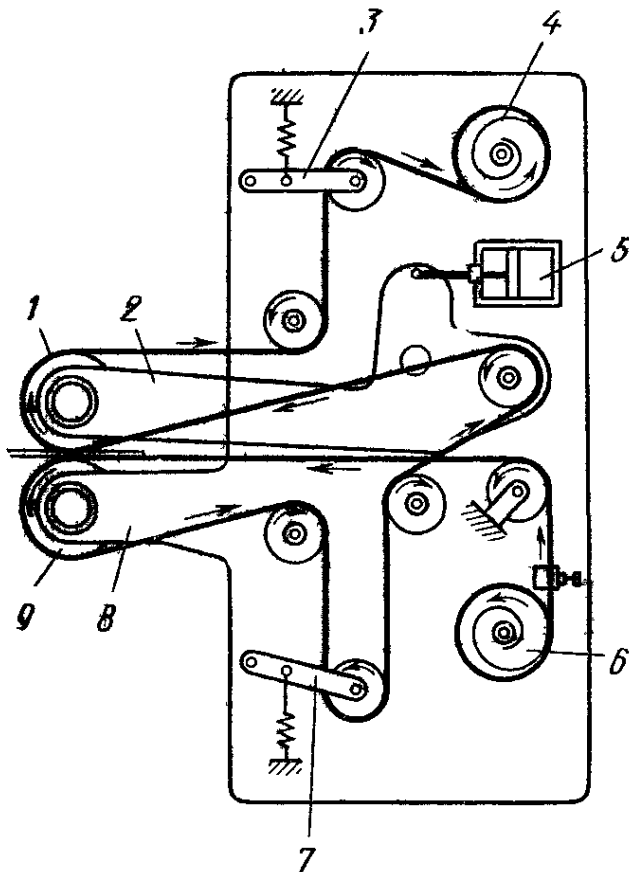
Схема машины для шовной сварки через медную проволоку:
